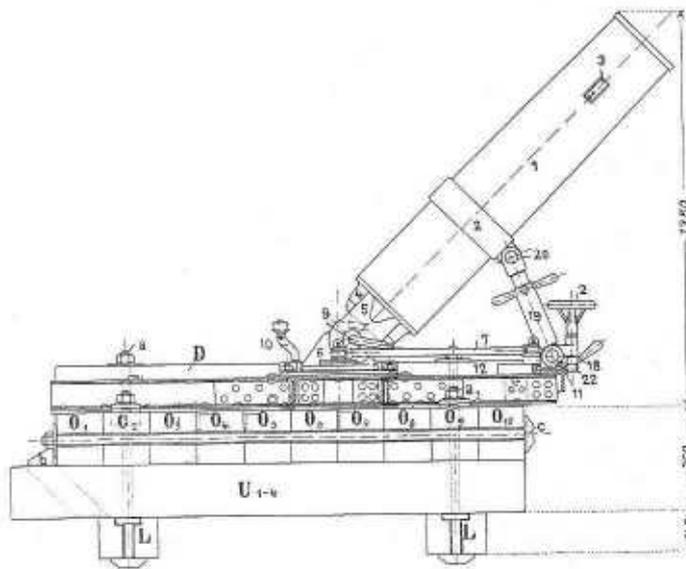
schwerer Flügelminenwerfer IKO, Seitenansicht,
